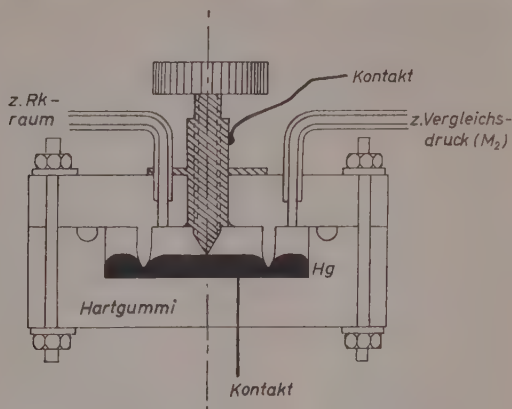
Druckfühler (ca. 60 mm \varnothing)
